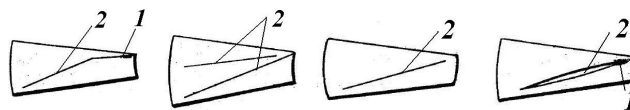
Види початкових заготовок у формі секторів із прорізами: 1 – зварний шов; 2 - прорізь
